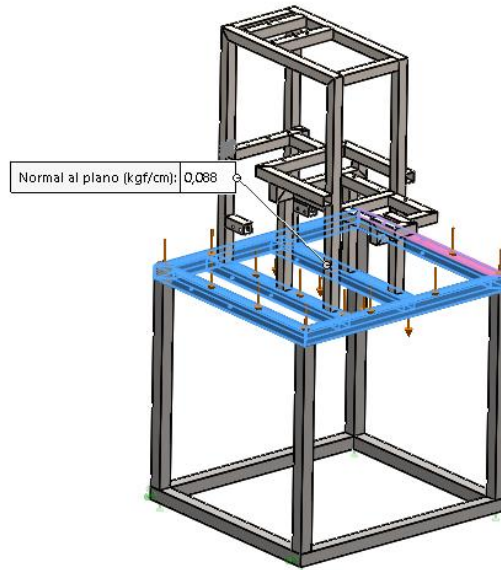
Fuerza aplicada en la parte inferior de la estructura.
